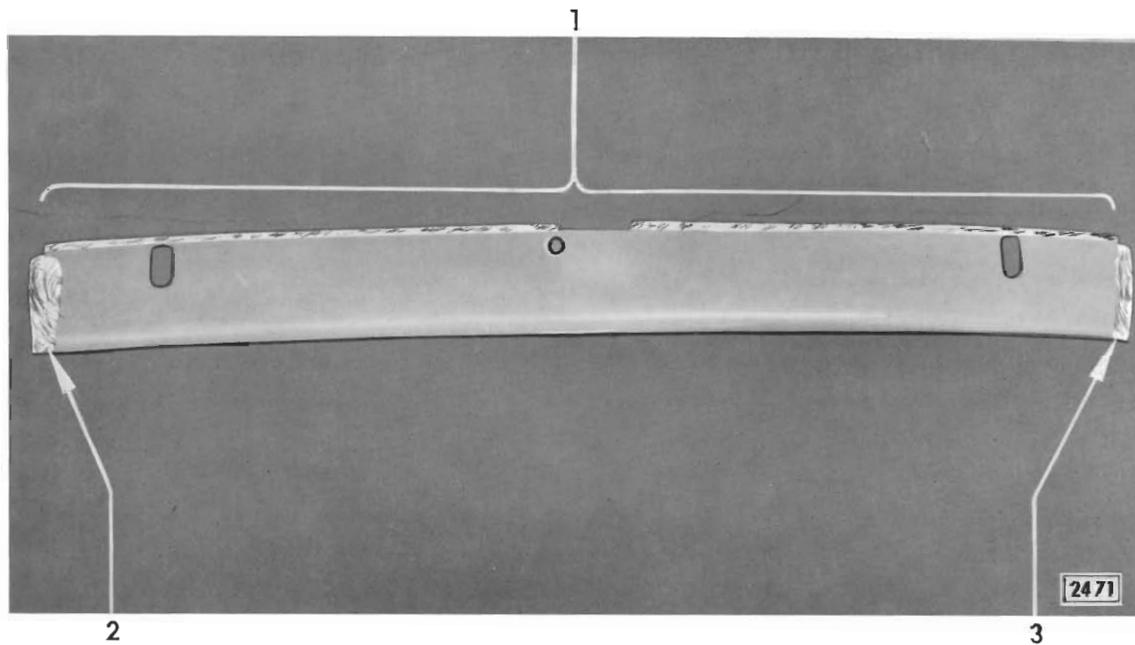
Anlageflächen und Flansche am Stoßstangenabdeckblech
